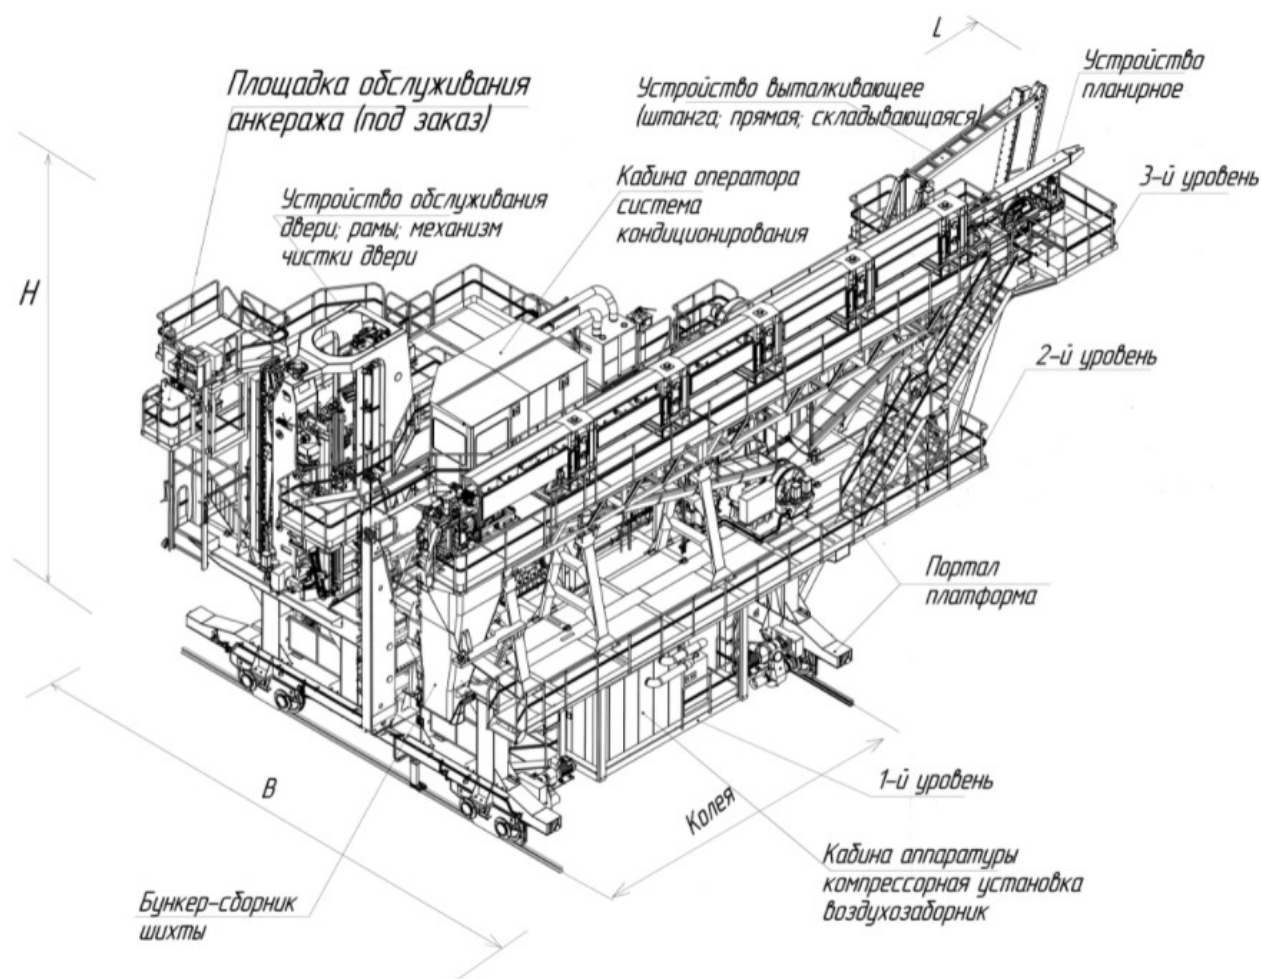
Креслення з позначеннями типового трьохповерхового виштовхувача коксу
